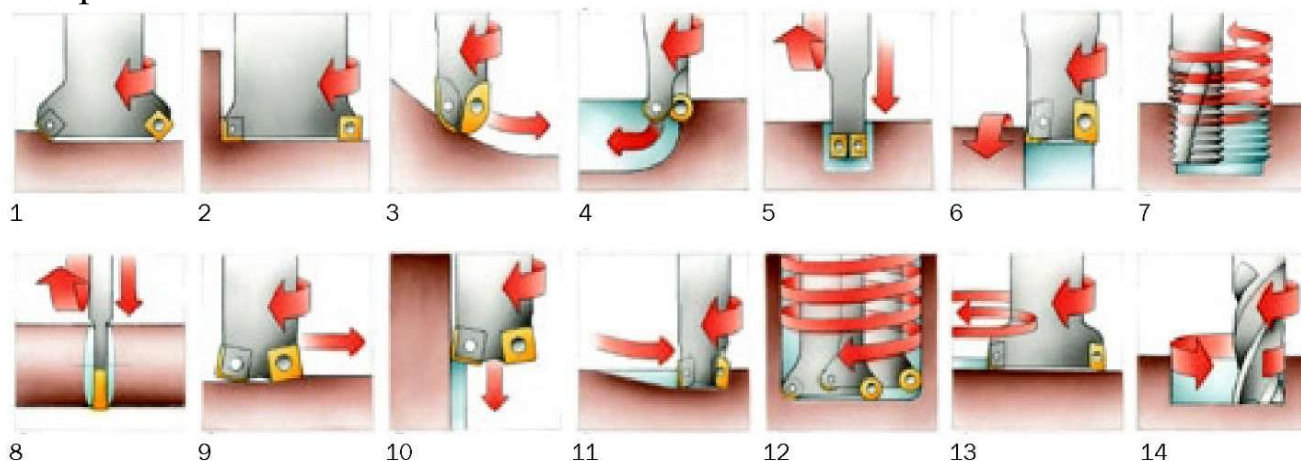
Основные типы фрезерных операций с точки зрения формы обрабатываемой поверхности и способа перемещения инструмента: 1-торцевое фрезерование; 2- фрезерование уступов; 3- профильное фрезерование; 4- фрезерование карманов; 5- фрезерование пазов; 6- фрезерование поверхностей вращения; 7- резьбофрезерование; 8- отрезка; 9- фрезерование с большими подачами; 10- плунжерное фрезерование; 11- фрезерование с врезанием; 12- винтовая интерполяция; 13- круговая интерполяция; 14- трохойдальное фрезерование
